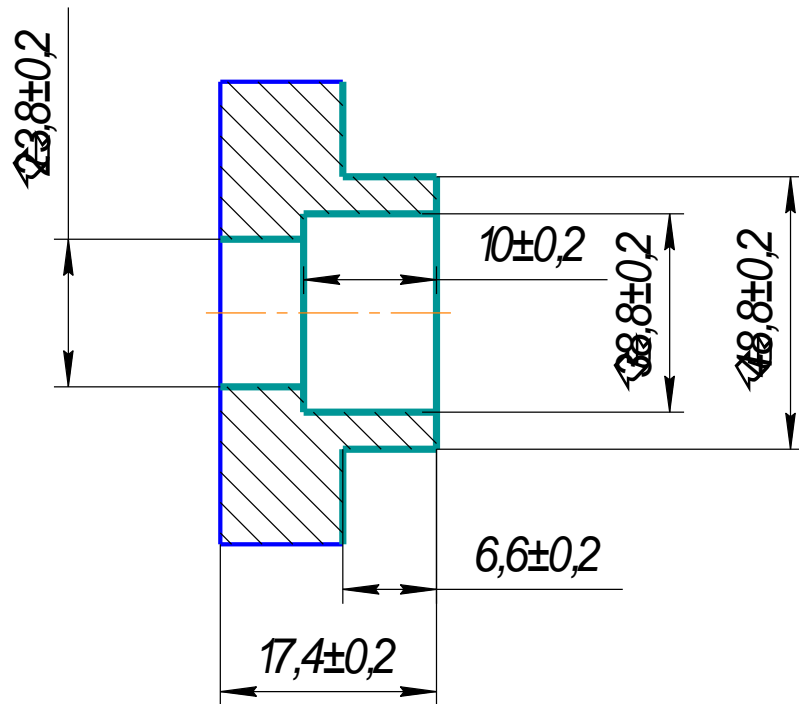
Заготовка кришки з призначеними припусками і допусками
